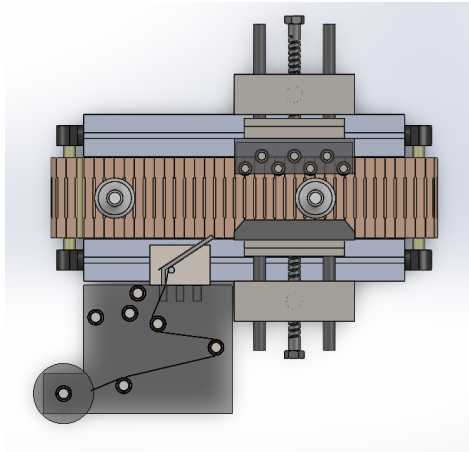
Sistema de etiquetado, vista alzado. Fuente: Propia.
